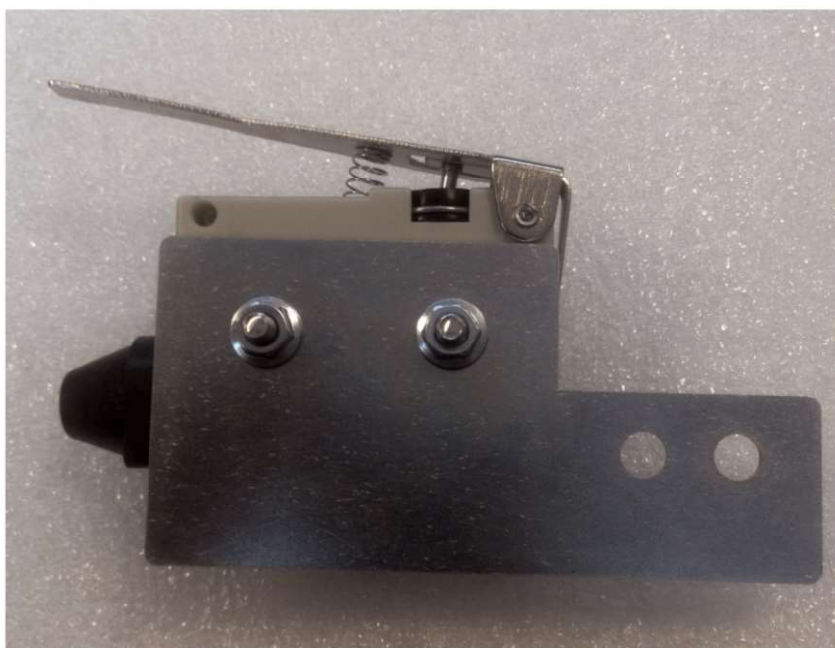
Присоединение датчика вскрытия к монтажной панели
